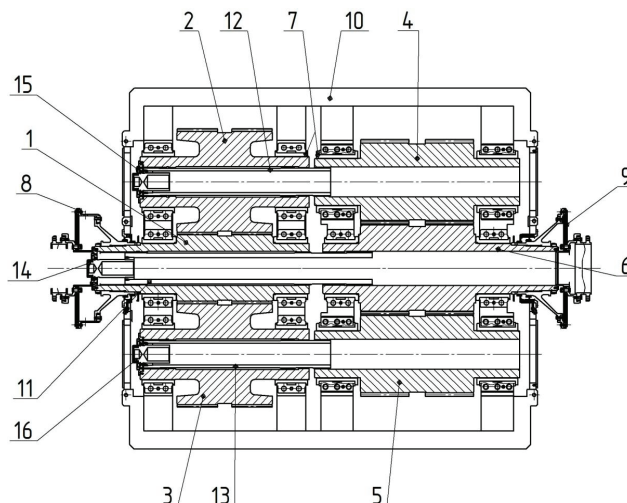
Конструкция редуктора со снятой крышкой: 1, 2, 3, 4, 5, 6 — зубчатые колёса; 7 — подшипники скольжения; 8, 9 — эластичные дисковые муфты; 10 — корпус; 11, 12, 13 — торсионные валы; 14, 15, 16 — механизмы переключения
